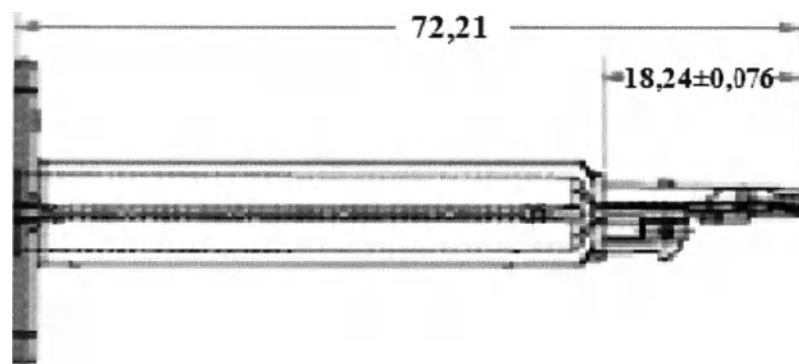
Корпус с загрузочной камерой и упором для пальцев
